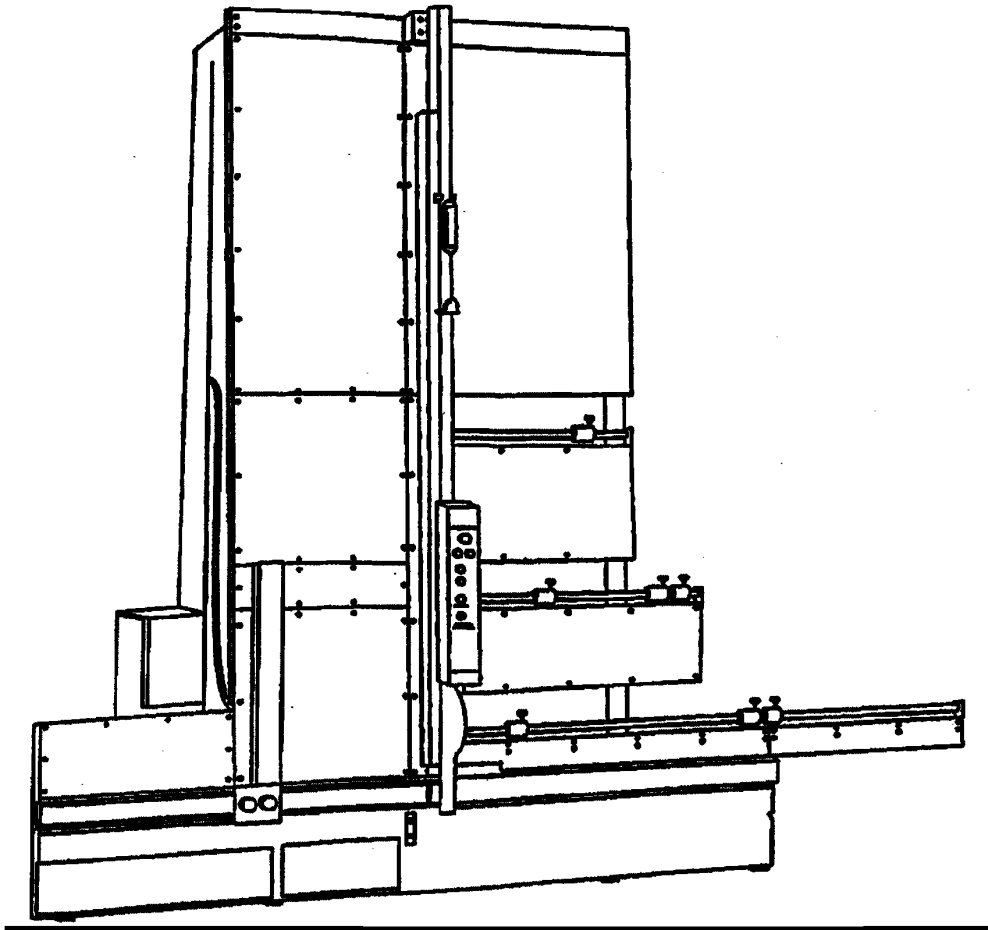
Пример круглопильного вертикального станка, у которого режущая часть дисковой пилы находится за обрабатываемым изделием
